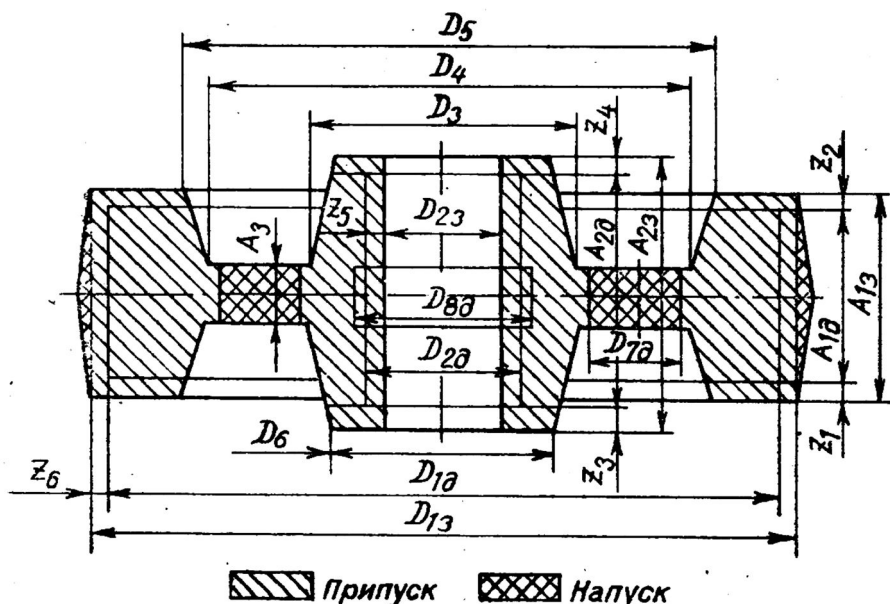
Заготовка шестерні. Розміри, напуски та припуски на обробку різанням
